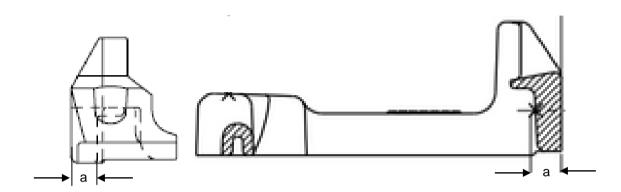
Поперечный разрез боковых изоляторов для скрепления Fastclip (Pandrol)
